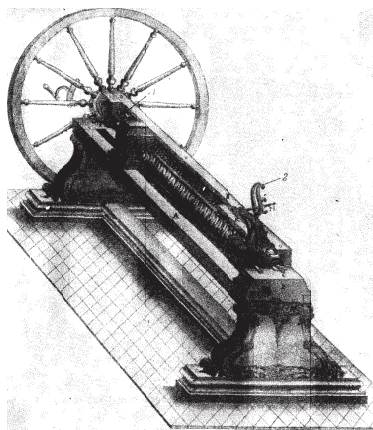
Токарно-винторезный станок с механизированным суппортом и сменными шестернями, предназначенный для производства деталей машин. Конструкция А. К. Нартова, 1738 г.
